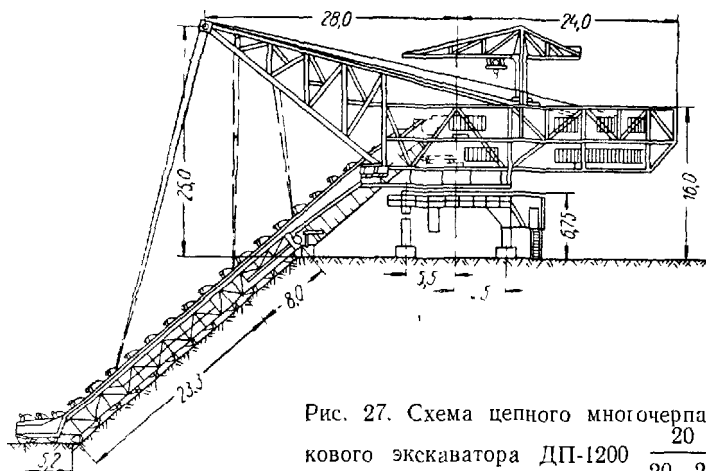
Схема цепного многочерпакового экскаватора ДП-1200
